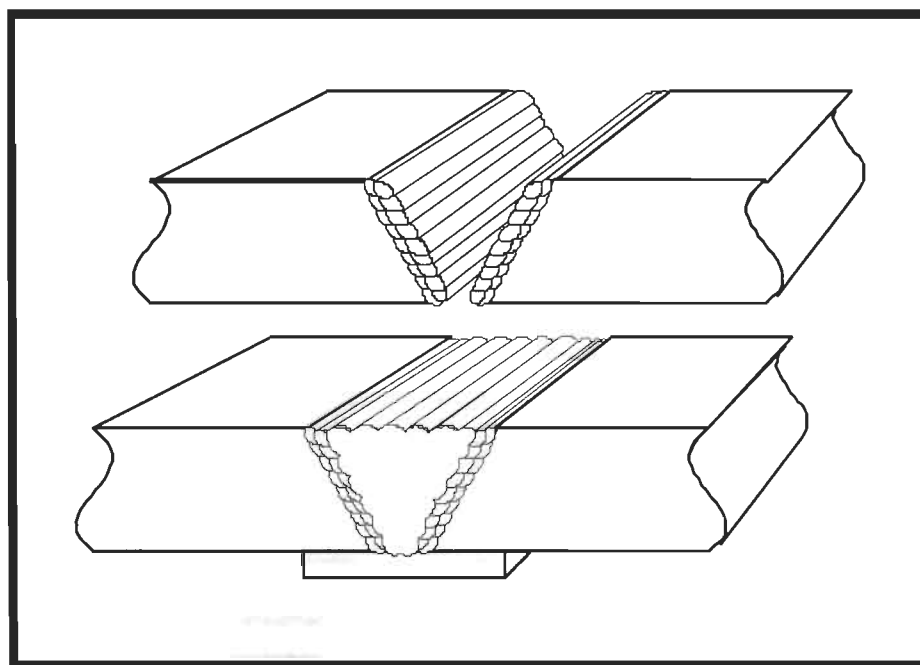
Representación esquemática de soldadura en capas [11].
